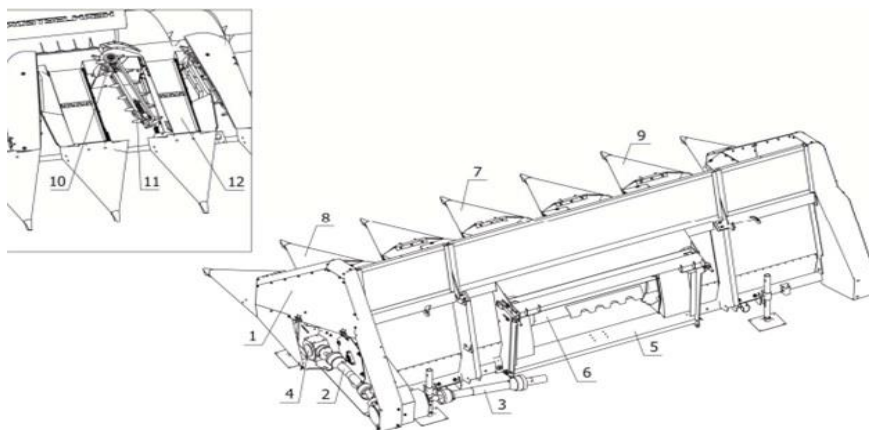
Общий вид жатки FALCON ПСП-670-05: 1 – корпус жатки; 2 – карданный вал боковой; 3 – карданный вал с предохранительной муфтой; 4 – боковой редуктор; 5 – переходная рамка; 6 – шнек; 7 – лифтер центральный; 8 – лифтер левый; 9 – лифтер правый; 10 – режущий аппарат; 11 – транспортер стеблей; 12 – транспортер семян
